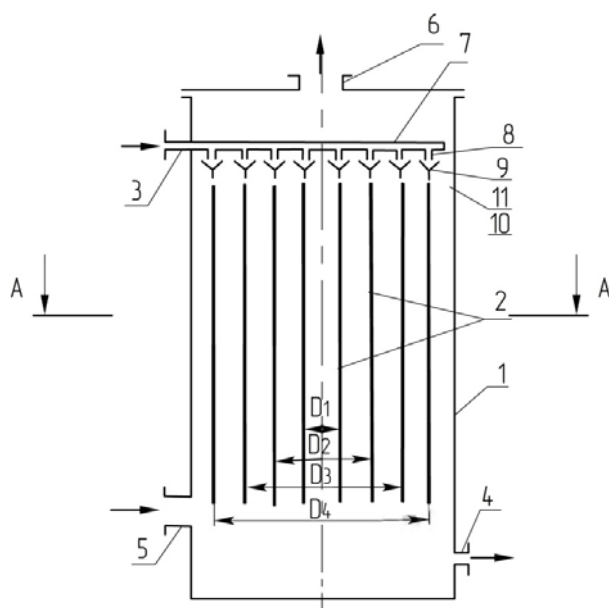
Предлагаемая конструкции колонны с трубчатыми рукавами
